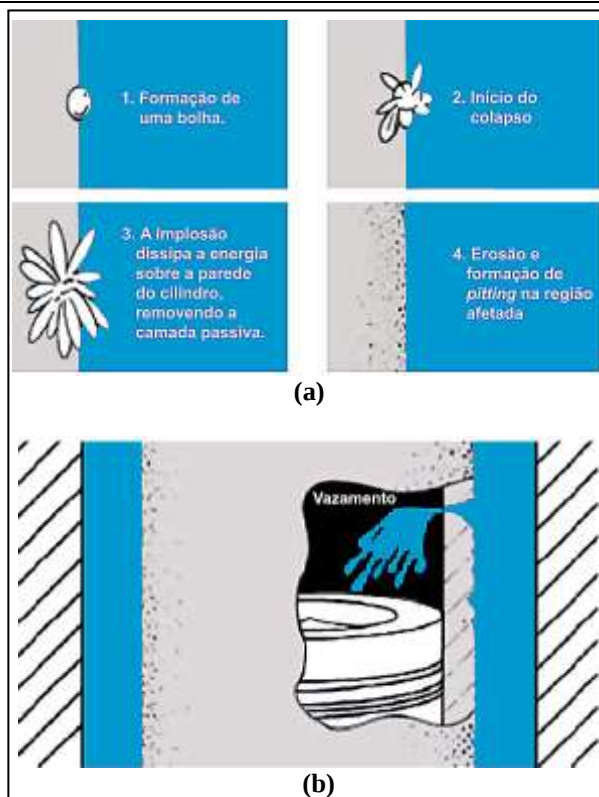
Progresso de cavitação e Pitting na parede de um cilindro de motor, adaptado de [2].
